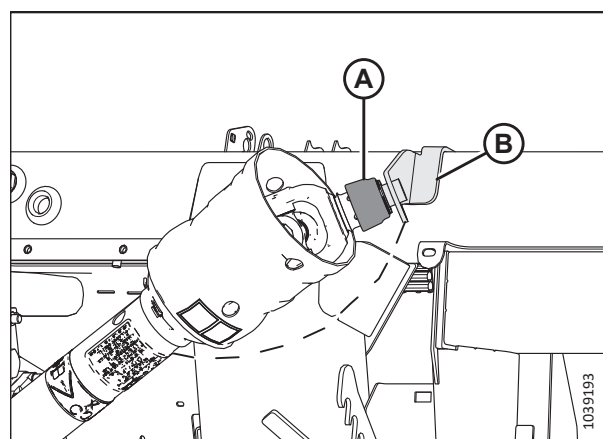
Jõuülekanne hoiuasendis – nõlva/kallaku jõuülekanne MACB7180, MACB7181 või MACB7326
